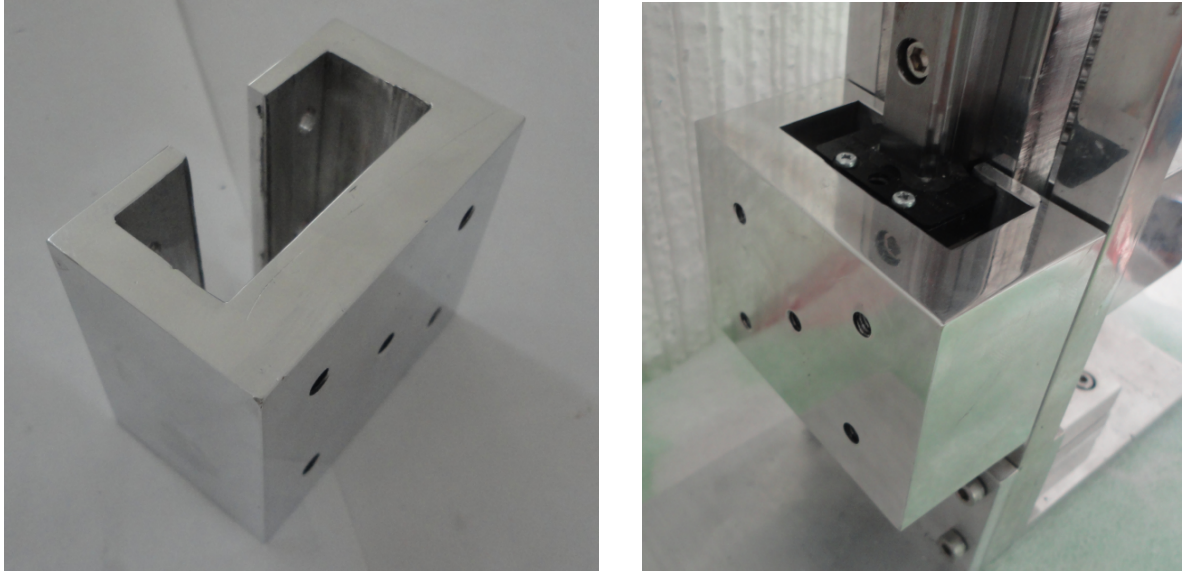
Soporte para montaje del motor piezoeléctrico
